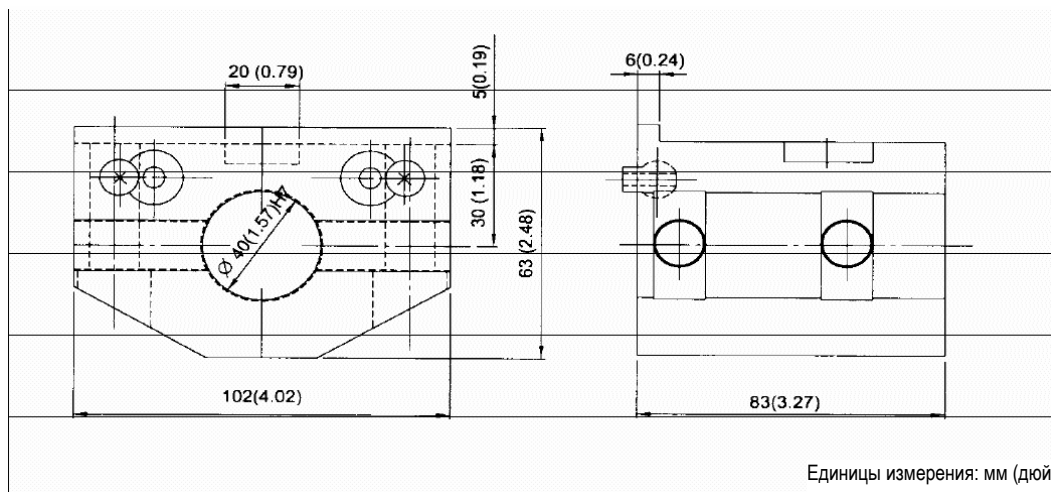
Габариты резцедержателя (резцедержатель типа II внешнего диаметра)
